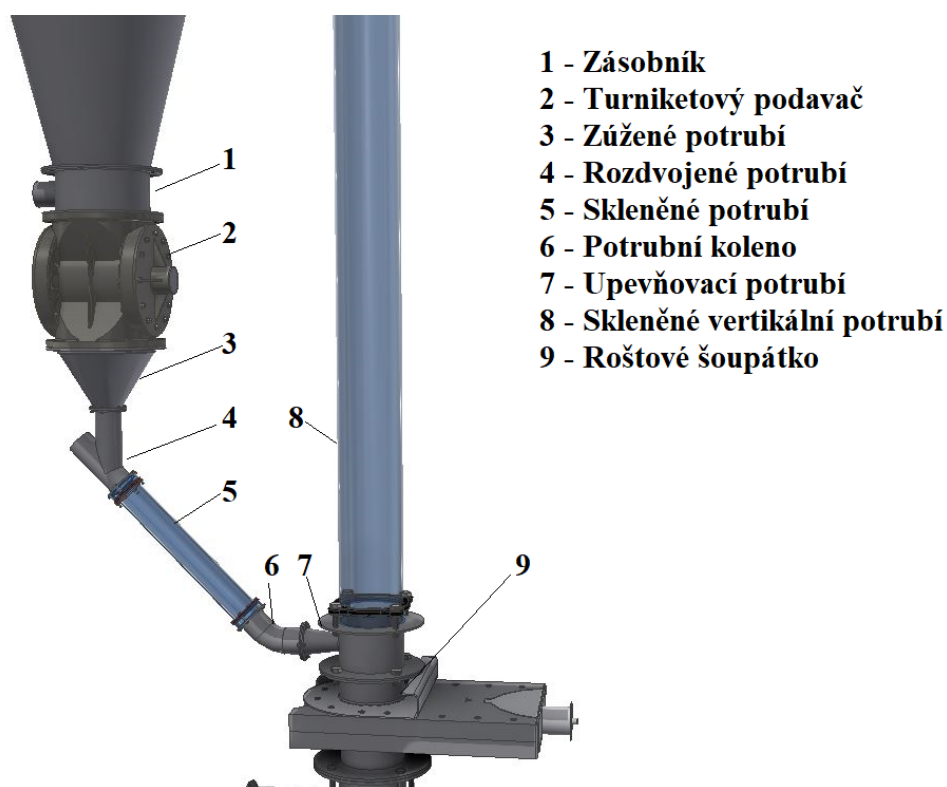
3D model upevňovací komponent [autor]
